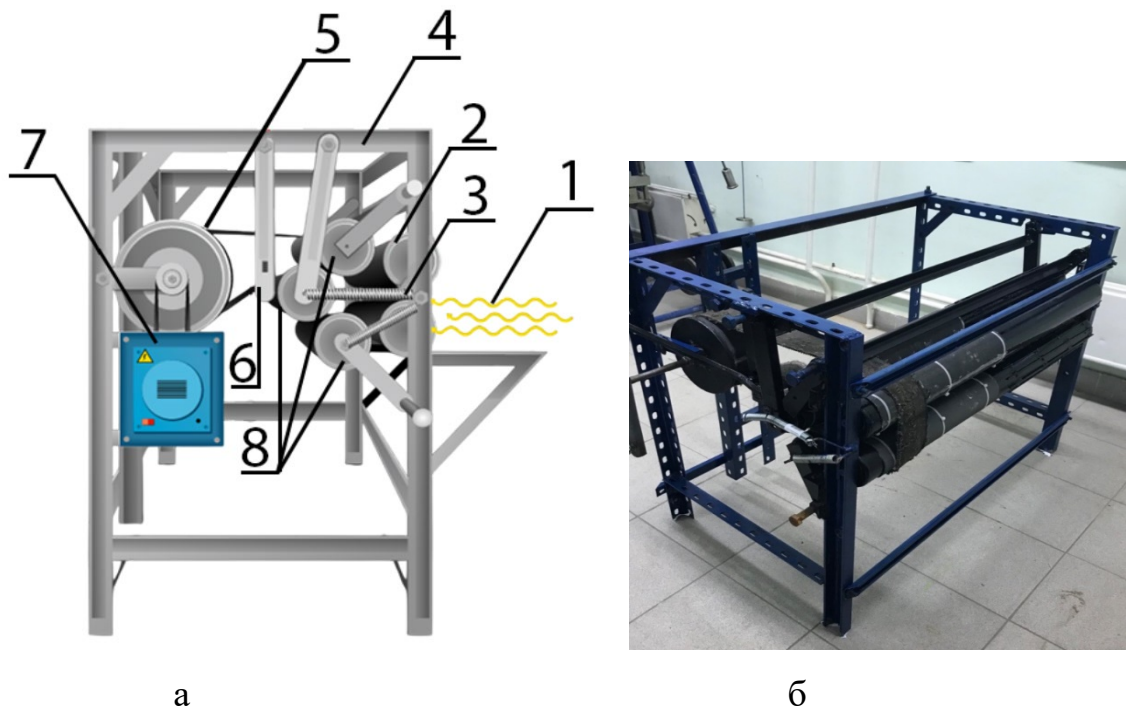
КПЗО для формування ПР із БССК: а – схема, б – загальний вигляд:
